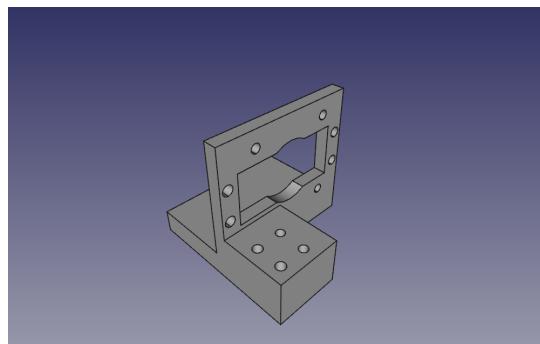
Alzado de pieza de sujeción del motor de la herramienta.
